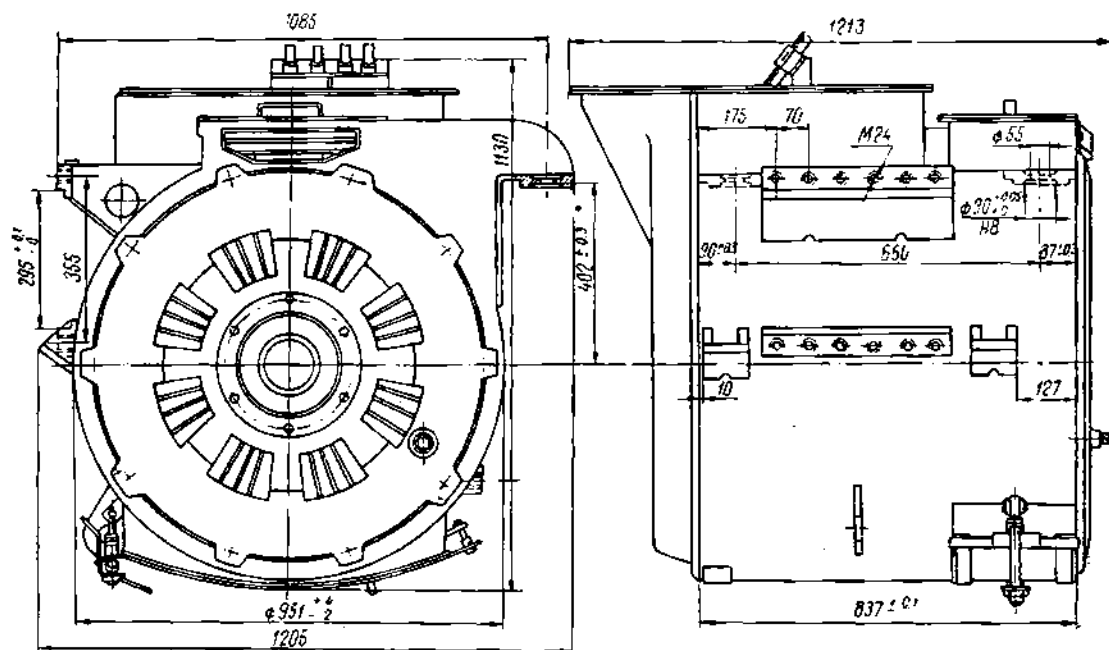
Motor tip LJE 108-1. Dimensiuni de montaj.
